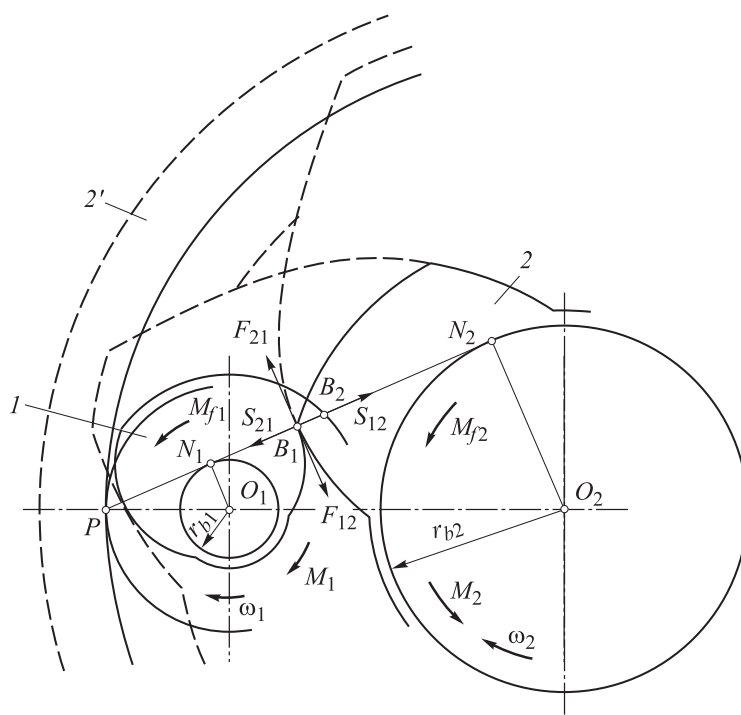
Цилиндрическая самотормозящая зубчатая передача
